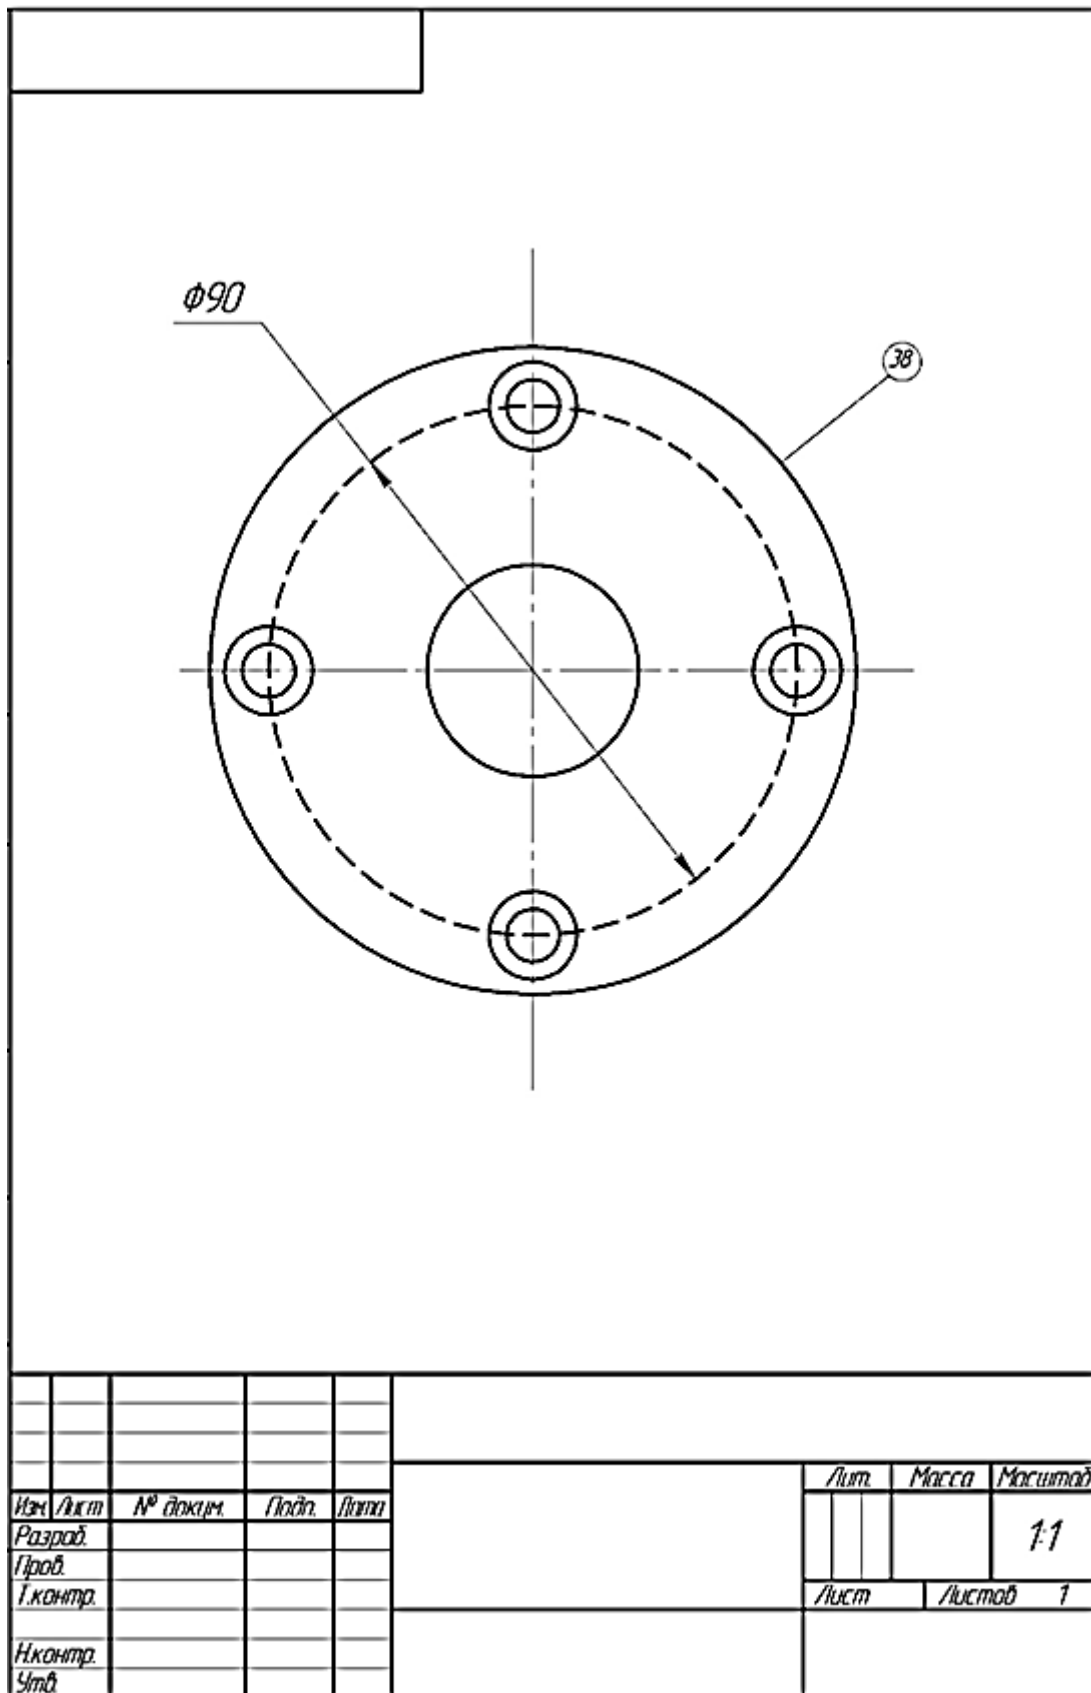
Рабочий чертеж крышки подшипника (вид сверху), с ошибками
